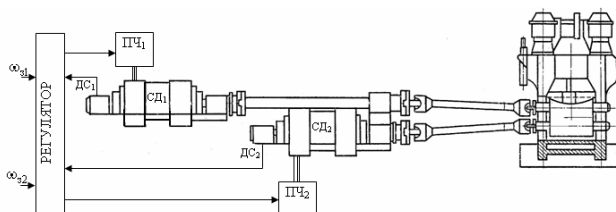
Схема главных приводов прокатного стана с синхронными двигателями и преобразователями частоты.
